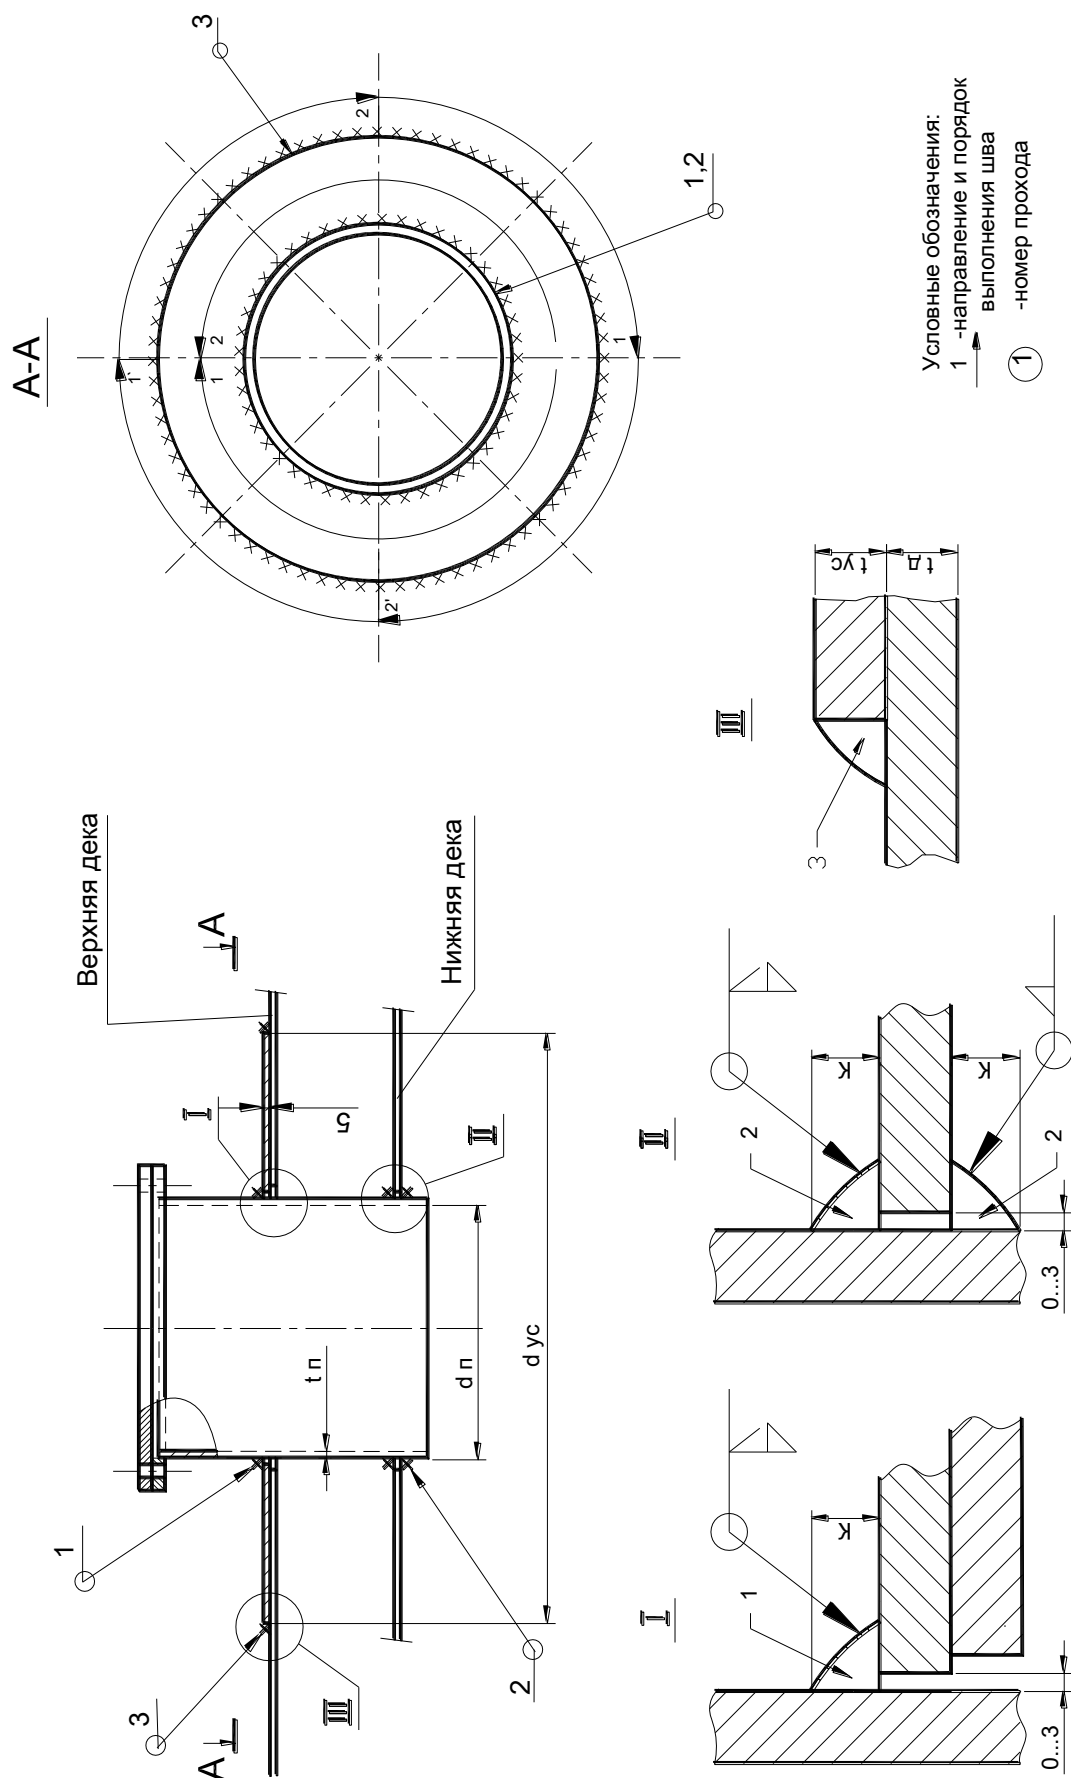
Схема сварки замерного люка-лаза
